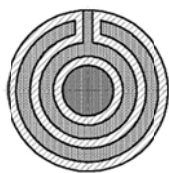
Двухслойная порошковая проволока с двойной оболочкой
